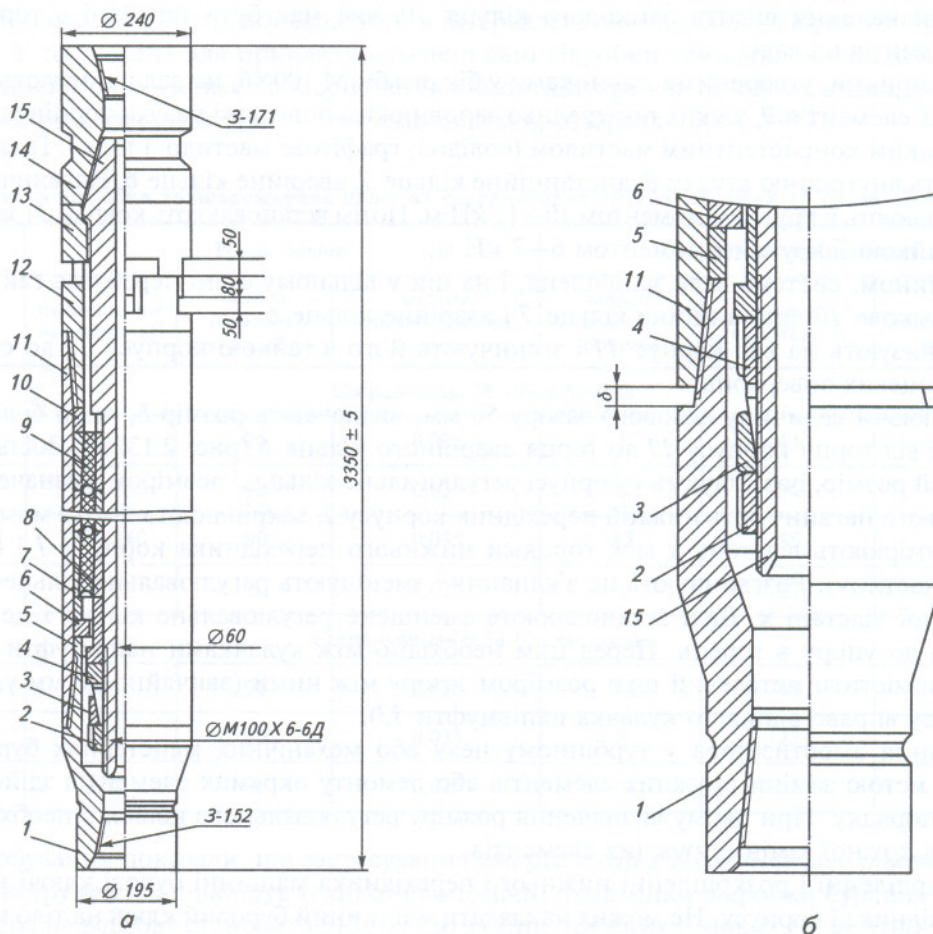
Схема наддолотного амортизатора НАБ-240:
